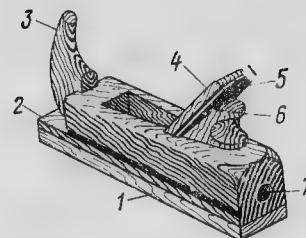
1 — подошва; 2 — корпус; 3 — рог; 4 — клин; 5 — нож; 6 — упор; 7 — пробка
